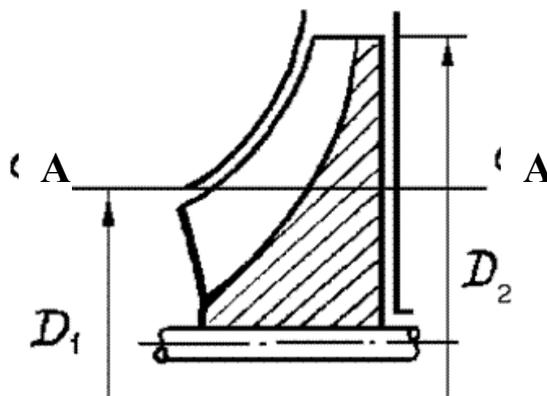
Сечение рабочего колеса центробежного компрессора цилиндрической поверхностью А-А.
